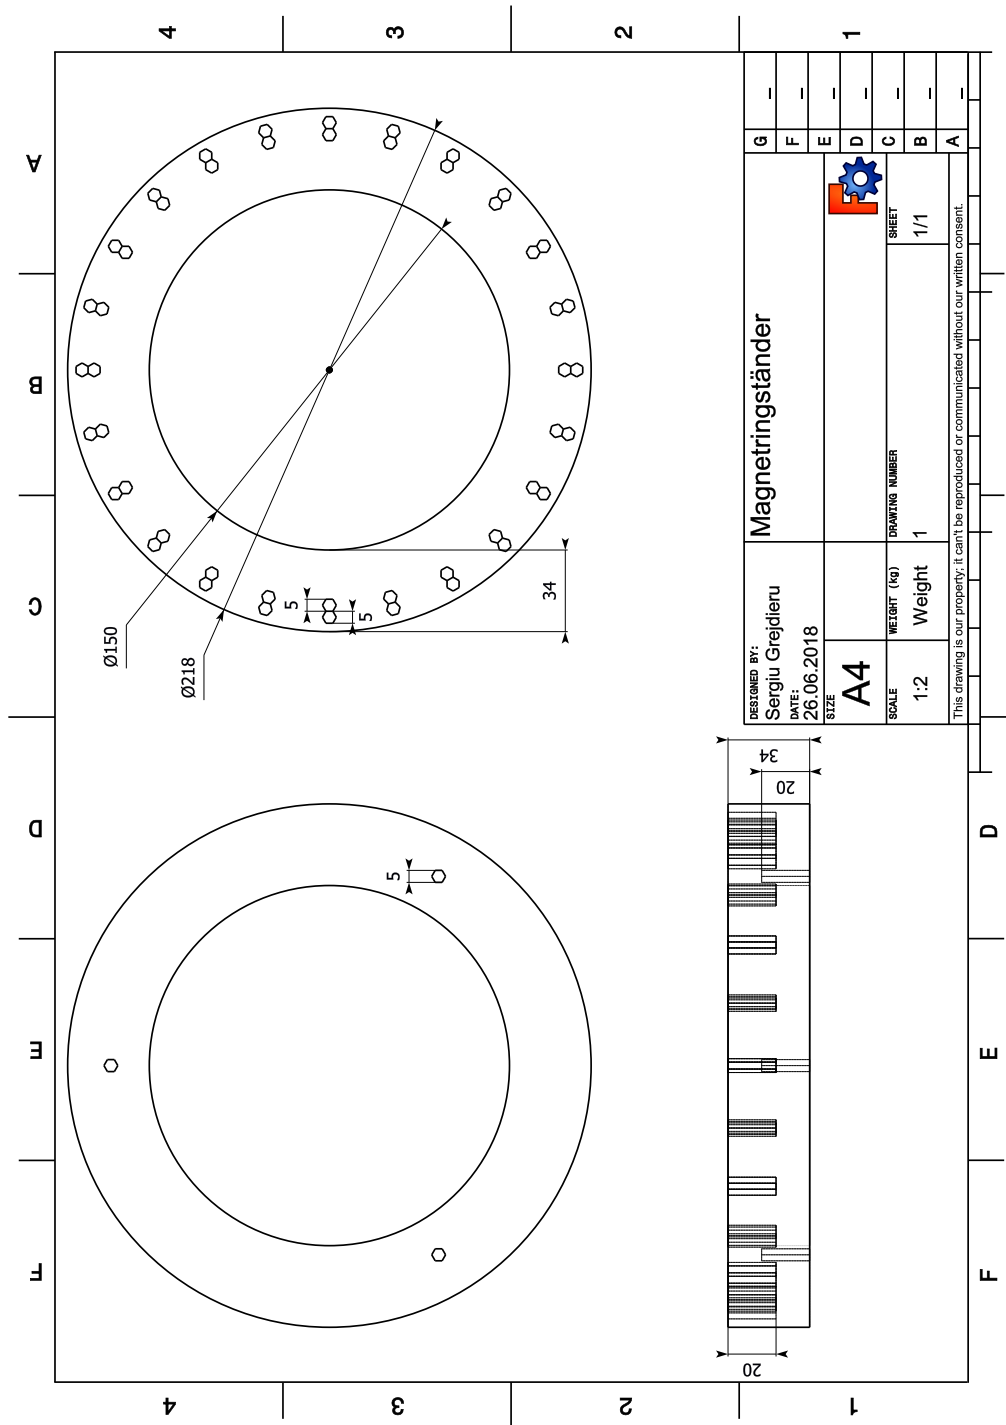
Technische Zeichnung: Magnetringsänder
